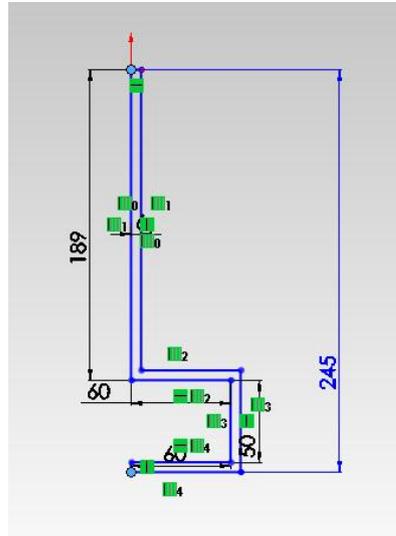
Geometría de perfil para Guardachoque.⁷⁸
